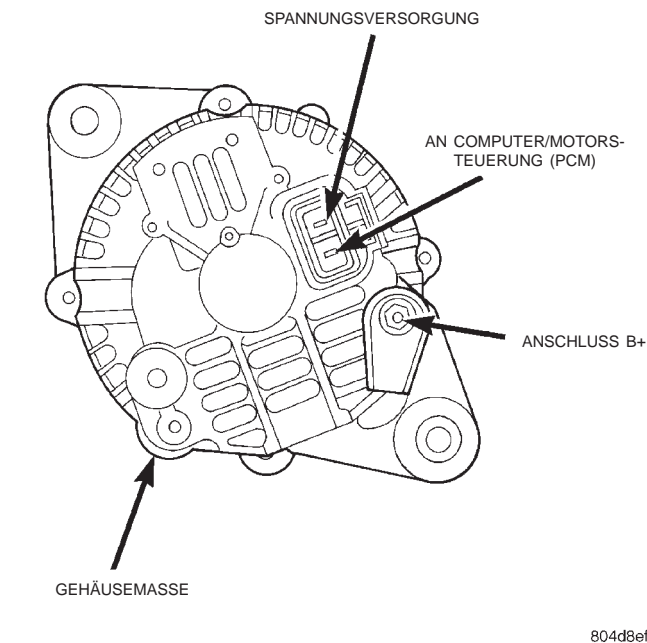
Anschlüsse der Lichtmaschine — 2.5L-Motor
